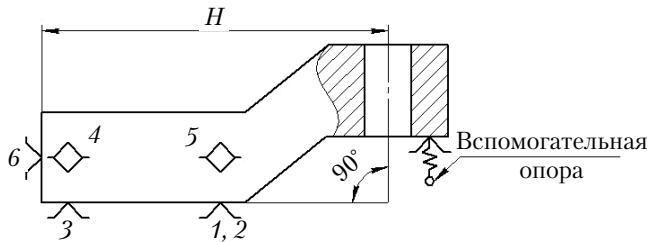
Схема установки заготовки в приспособлении для сверления отверстия с использованием вспомогательной опоры
